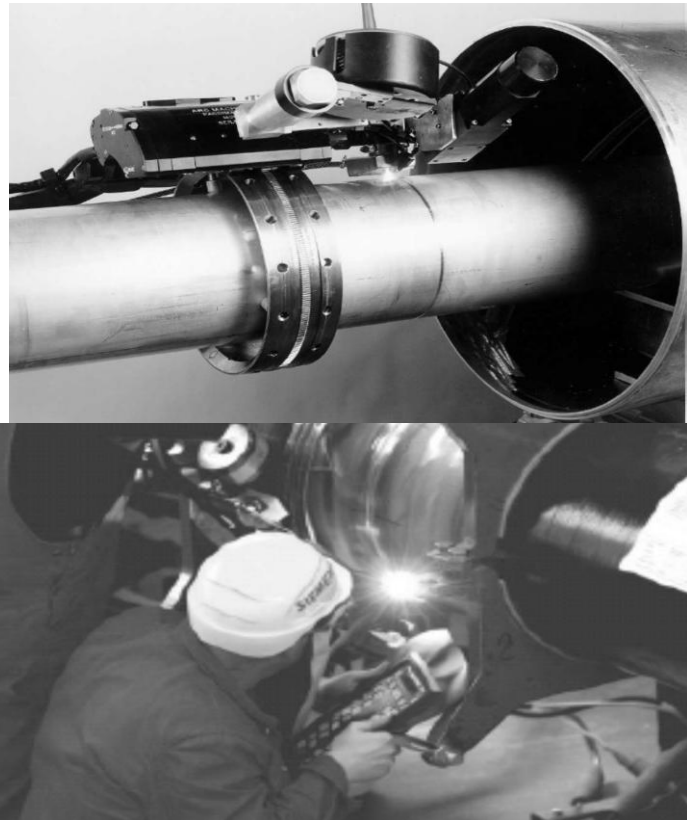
Процесс автоматизированной сварки модулей ГИЛ
